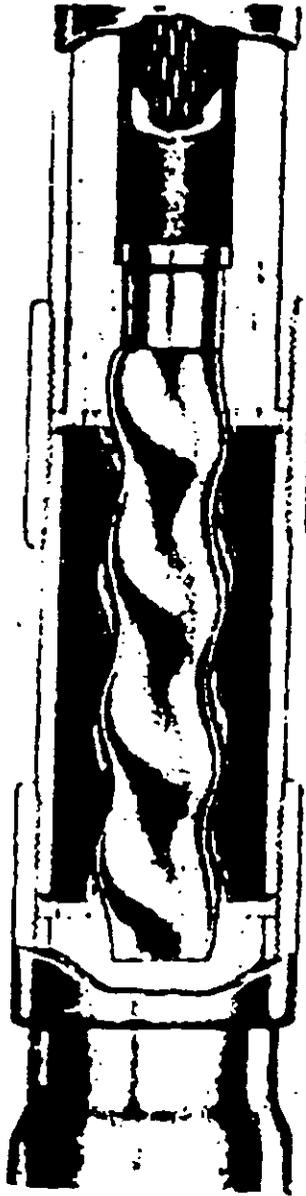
Bomba de pozo profundo de rotor helicoidal. (Cortesía de Peerless Pump División, Food Machinery and Chemical Corp.).
